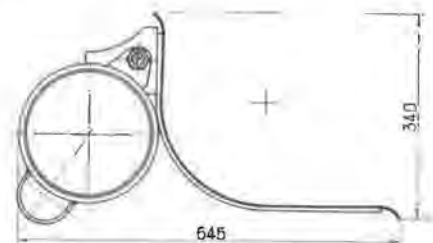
Coupe montrant l'assemblage des couloirs de glissement au tube de retour de la chaîne à disques. Assemblage dit « couloirs équerres ».
